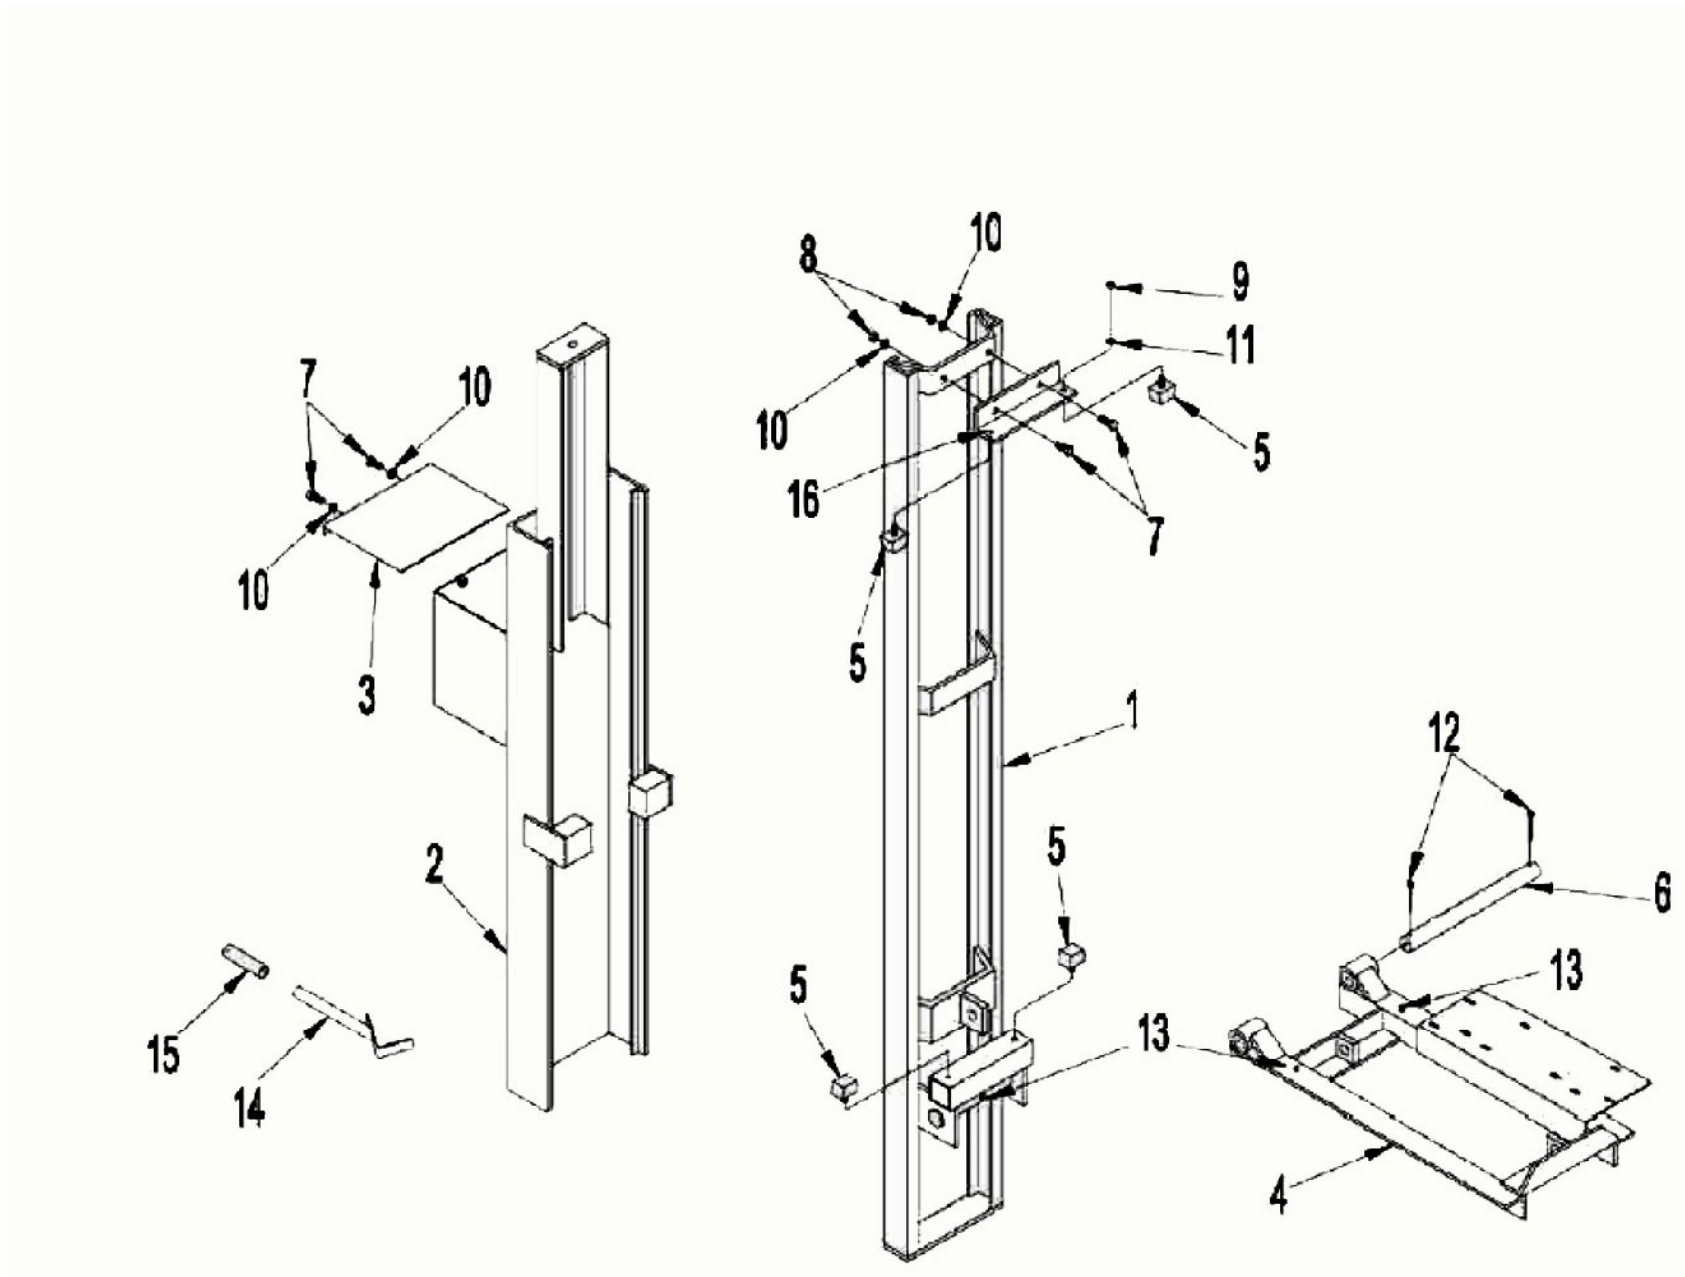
Чертеж молота в сборе нераздвижного типа
